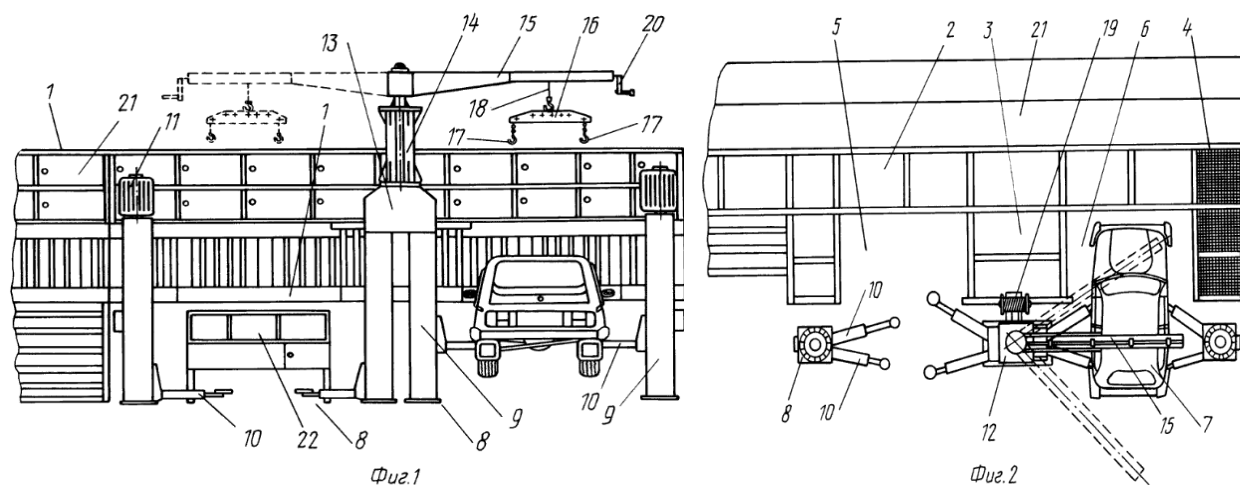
Сборочный стенд для монтажа автомобилей
